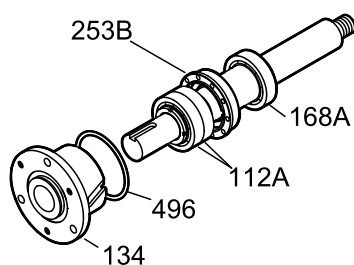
Extracción de la carcasa del rodamiento y del rodamiento
